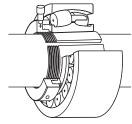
Tuerca hidráulica que se utiliza para montar el rodamiento en un manquito de arrastre.
